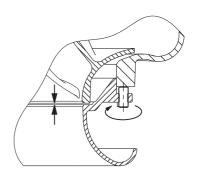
Осевой зазор рабочего колеса, типы установок S, C и ST
